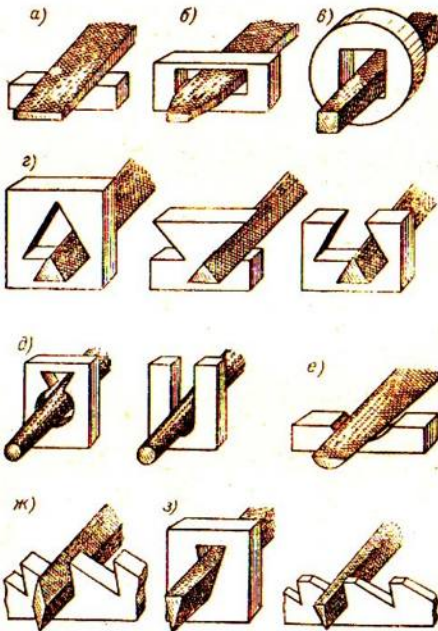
Формы сечения напильников и примеры их применения: а, б-плоские; в-квадратный; г-трёхгранный; д-круглый; е-полукруглый; ж-ромбический; з-ножовочный
